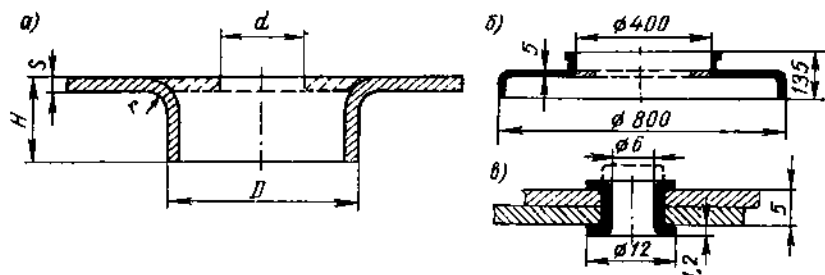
Примеры операций отбортовки: а — в плоской заготовке; б — в котельном днище; в — при полый заклепке
